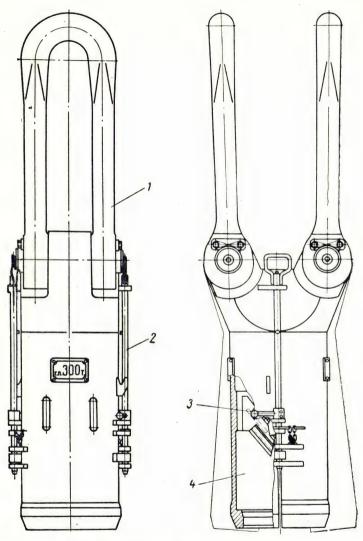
Элеватор буровой установки: i — штроп; i — штырь; i — рукоятка; i — корпус
